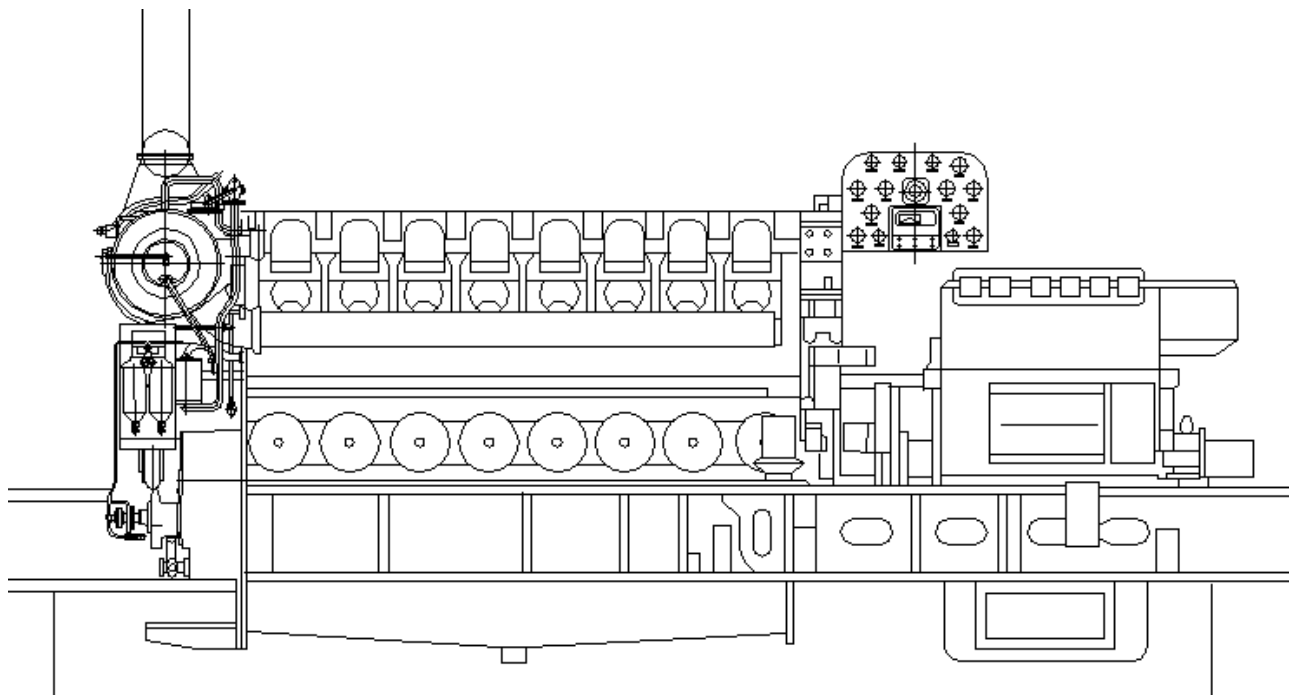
Загальний вигляд двигун-генератора ДвГА - 500
